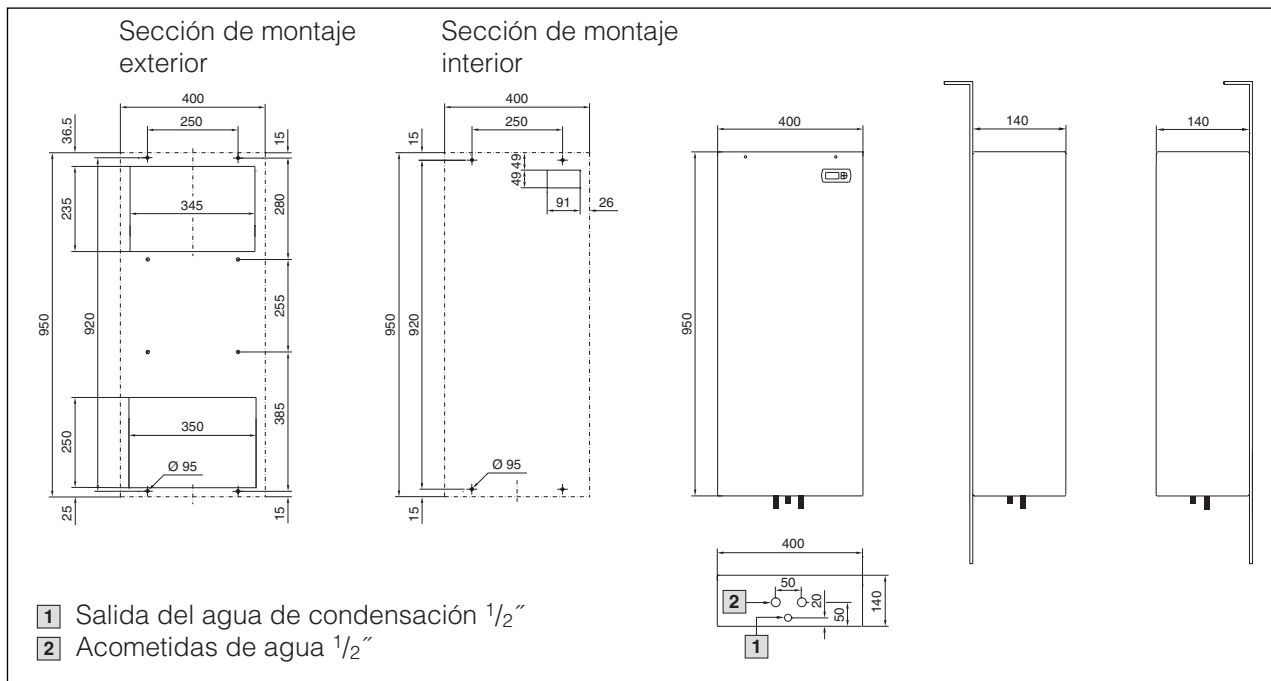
SK 3373.xxx/SK 3374.xxx montaje exterior
